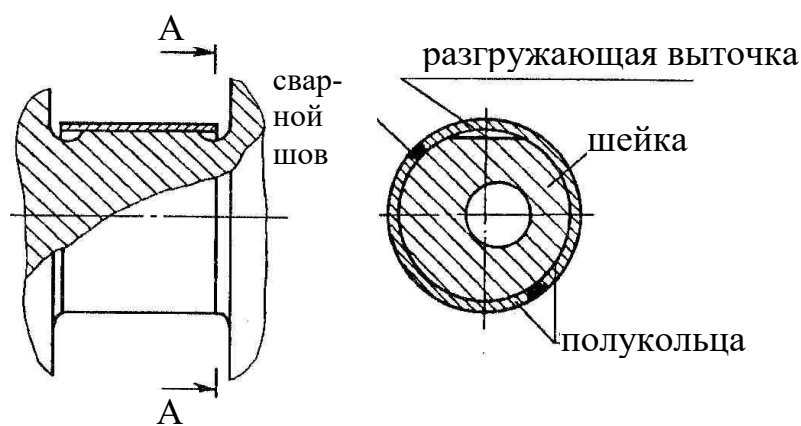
Схема восстановления шеек коленчатого вала двигателя приваркой стальных полуколец
